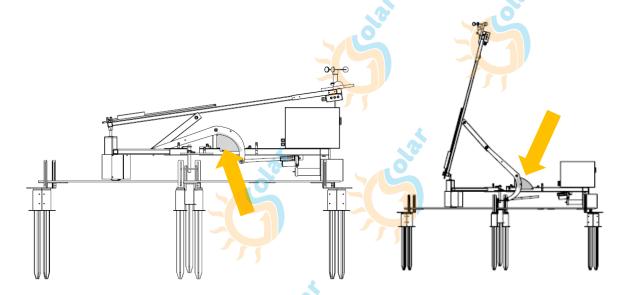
Vista protezione meccanica fissa movimento inclinazione
